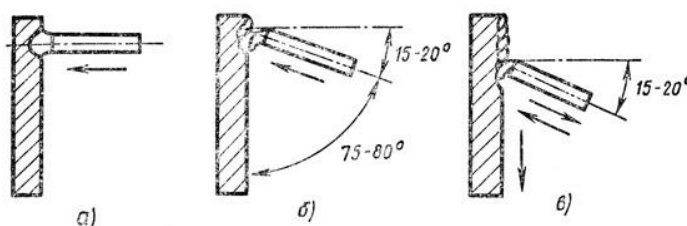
Схема техники сварки (наплавки) на спуск: а - зажигание дуги, б - образование сварочной ванны, в - движение электрода вниз
